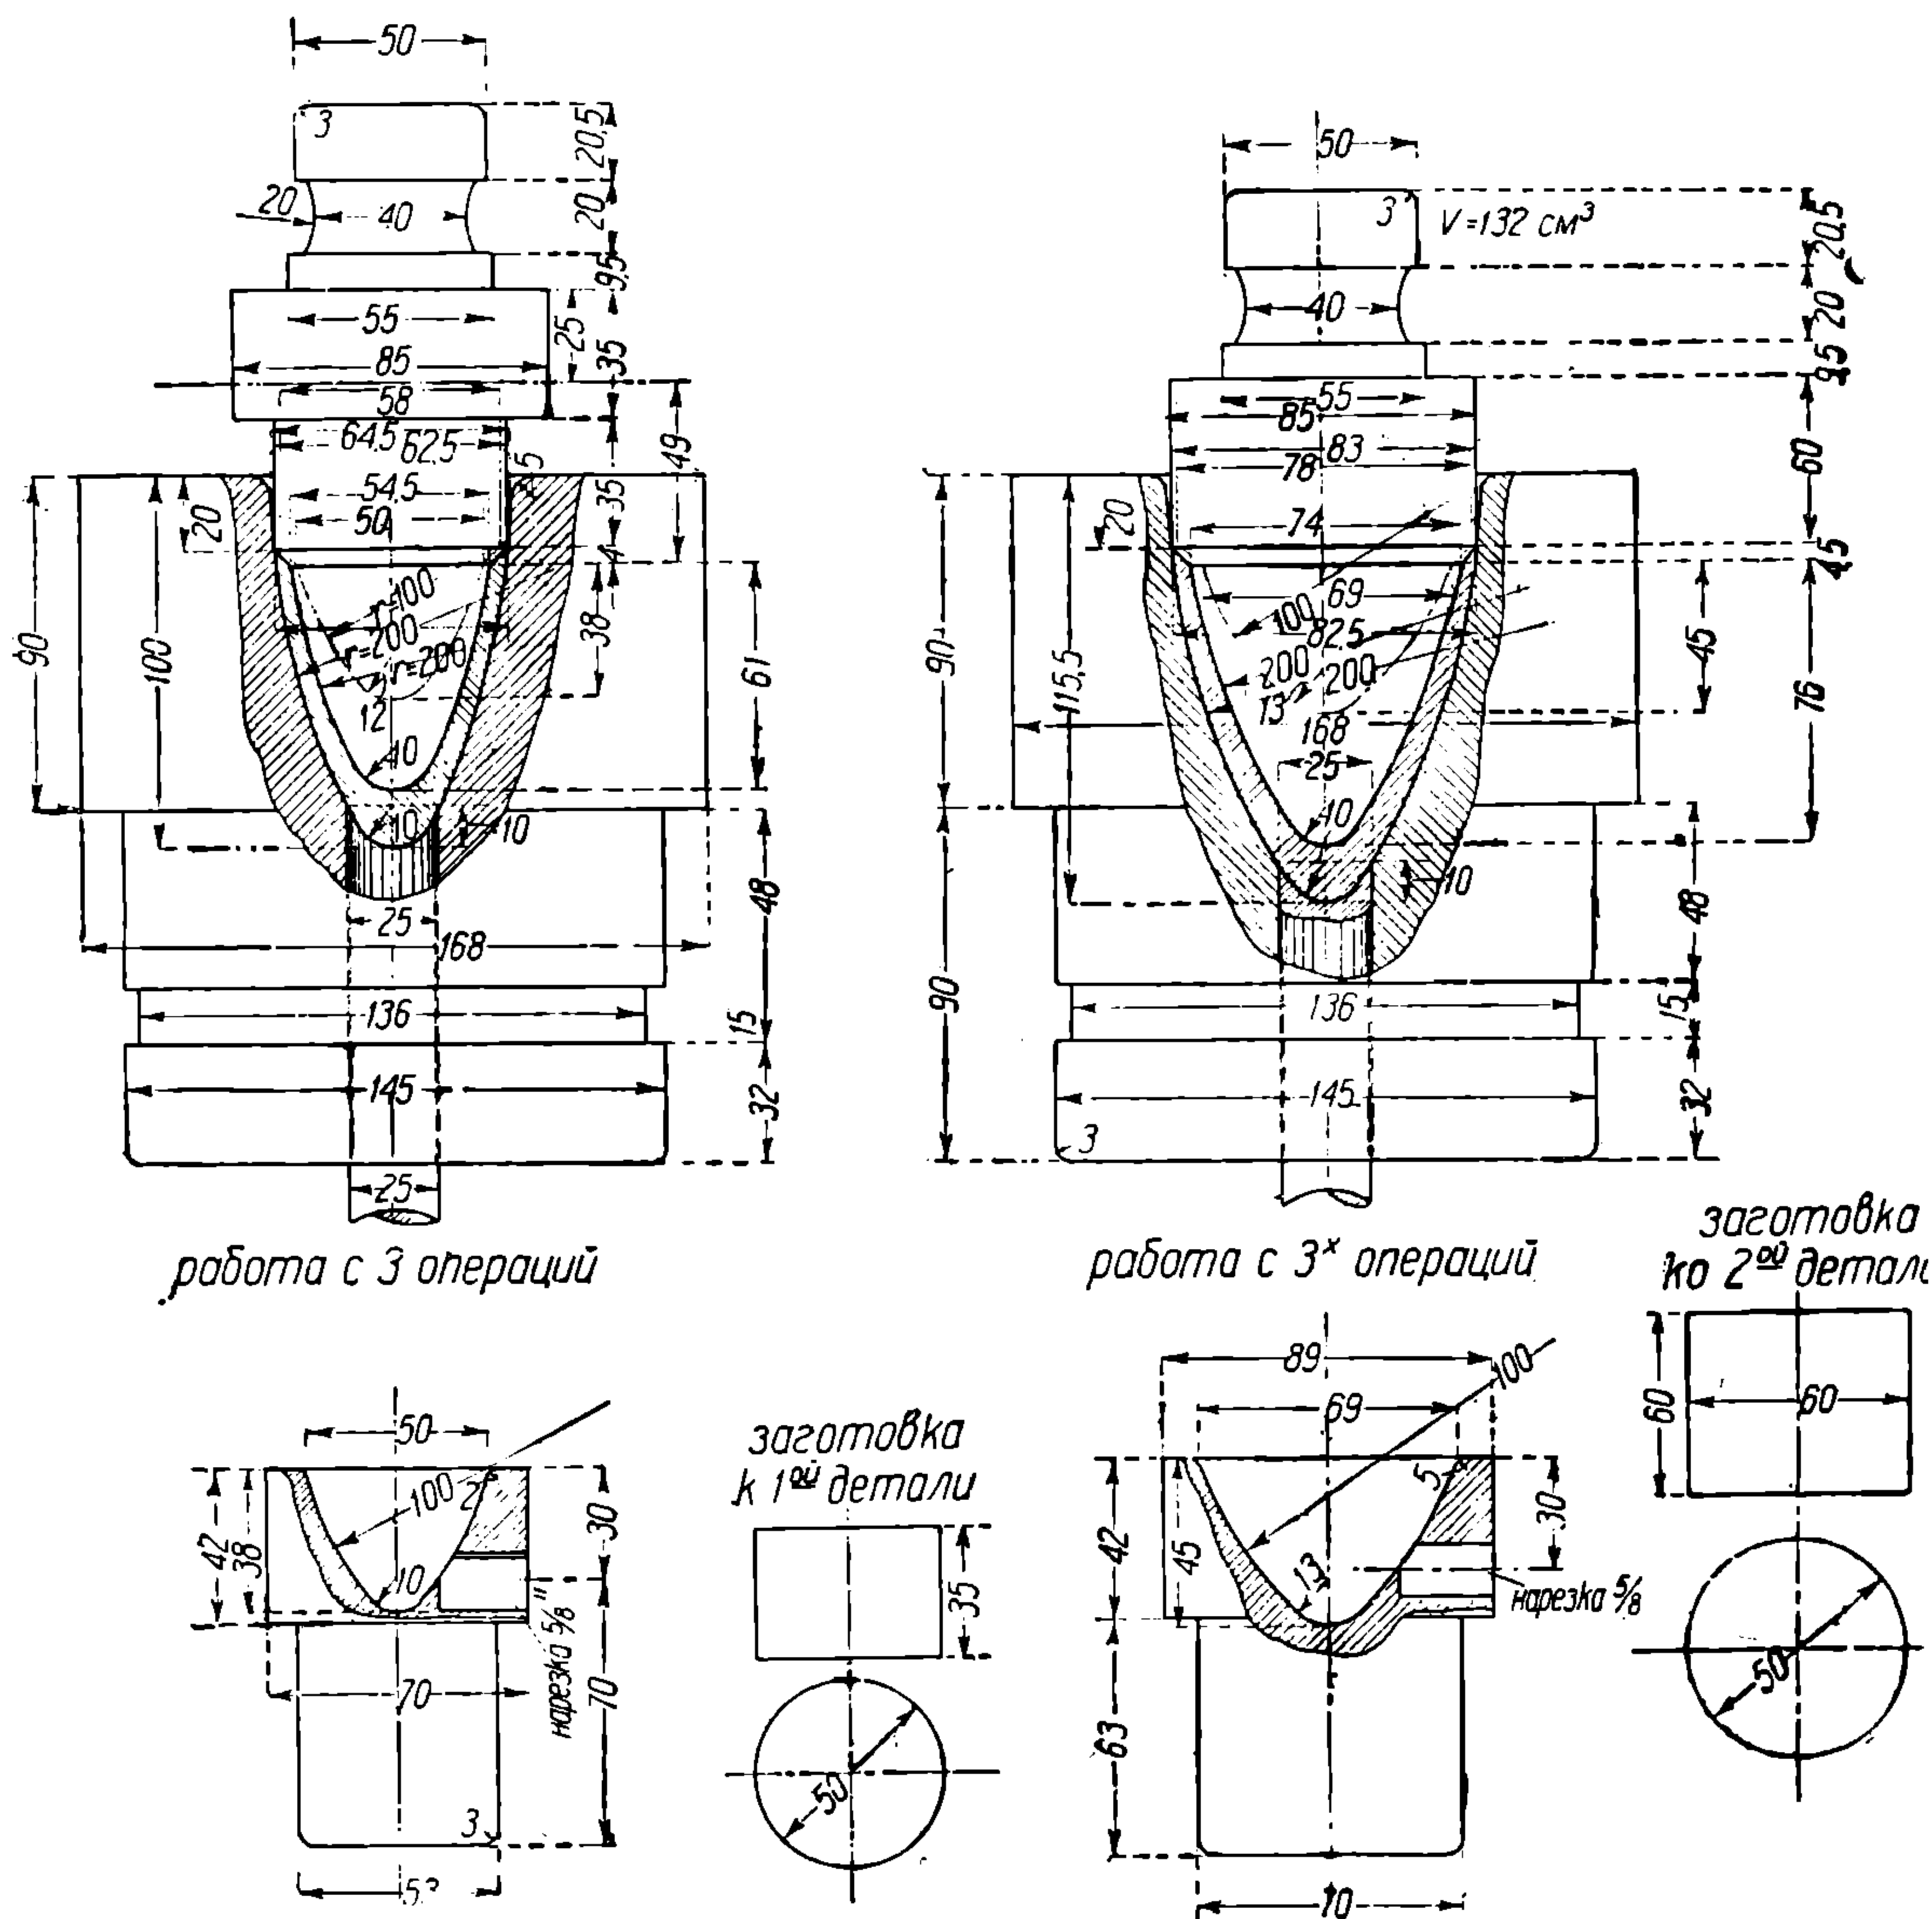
Последовательность изготовления заднего колпачка элемента штамповкой.
